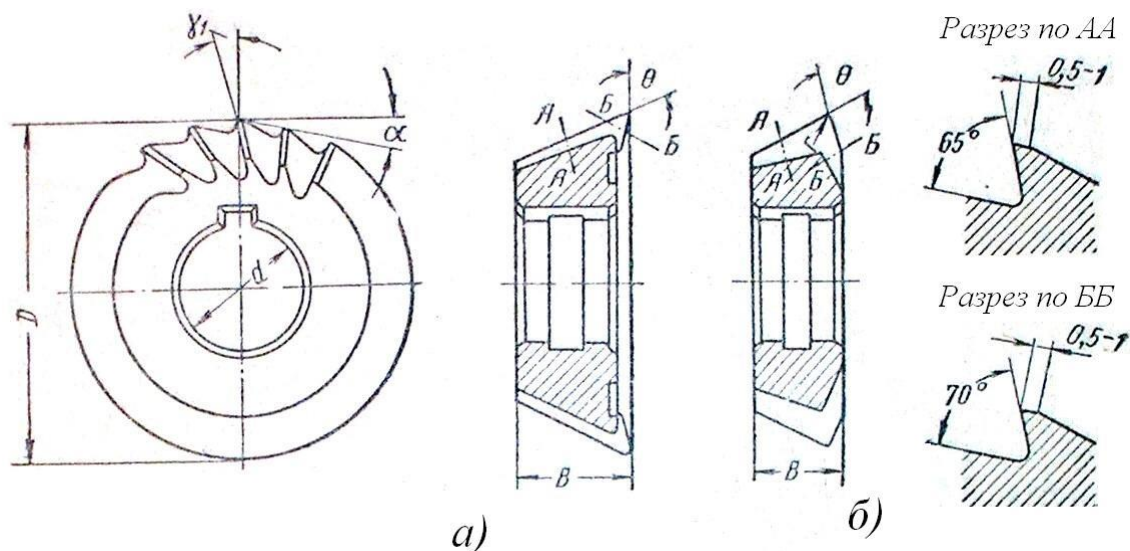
Угловые фрезы: а – одноугловая; б – двухугловая, несимметричная.
